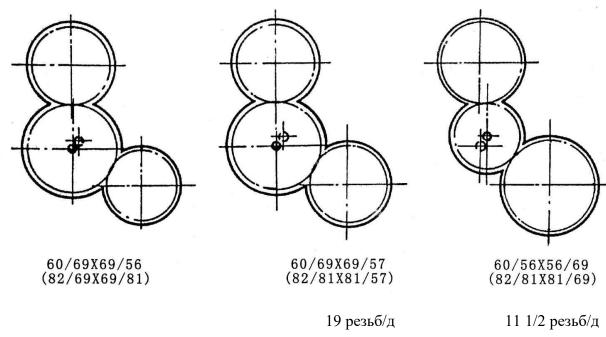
Зацепление сменных зубчатых шестерен станка СЈ6½ 66YB
